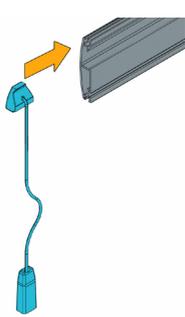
Anbringen der Zugschnur zusammengebaut mit der Halterung und dem Griff
